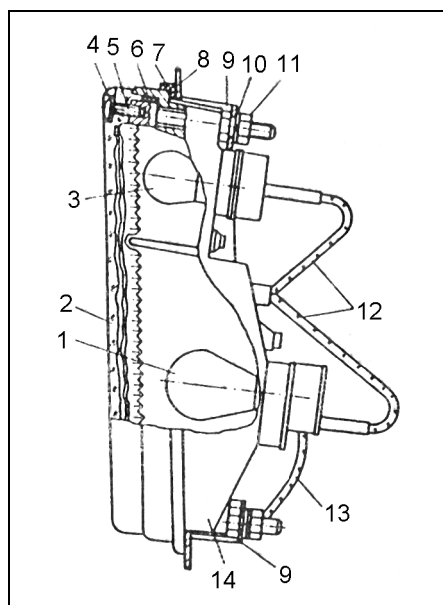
Подфарник: 1 – лампа указателя поворота; 2 – рассеиватель левый; 3 – лампа освещения габарита автомобиля; 4 – шайба; 5 – винт; 6 – прокладка рассеивателя; 7 – прокладка корпуса подфарника; 8 – облицовка передка; 9 – кронштейн крепления подфарника; 10 – шайба пружинная; 11 – гайка крепления подфарника; 12 – провода основного пучка проводов; 13 – провод на массу; 14 – корпус подфарника в сборе (левый).
